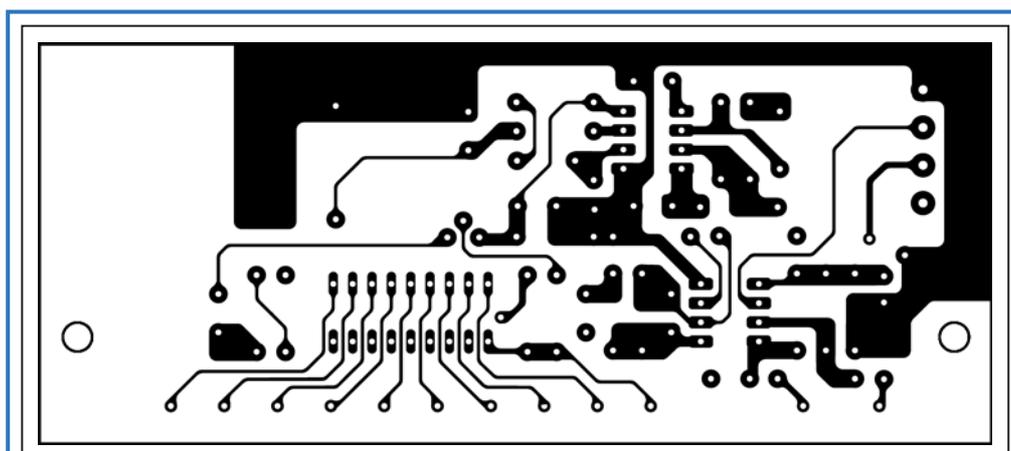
Dessin, à l'échelle 1, de la face soudures la platine voltmètre/buzzer.
